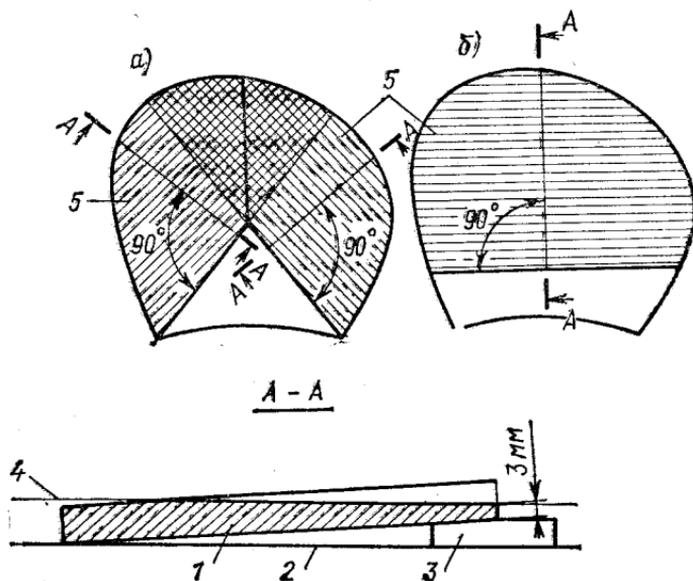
Предварительная обработка заготовки лопасти: а и б — варианты обработки.
